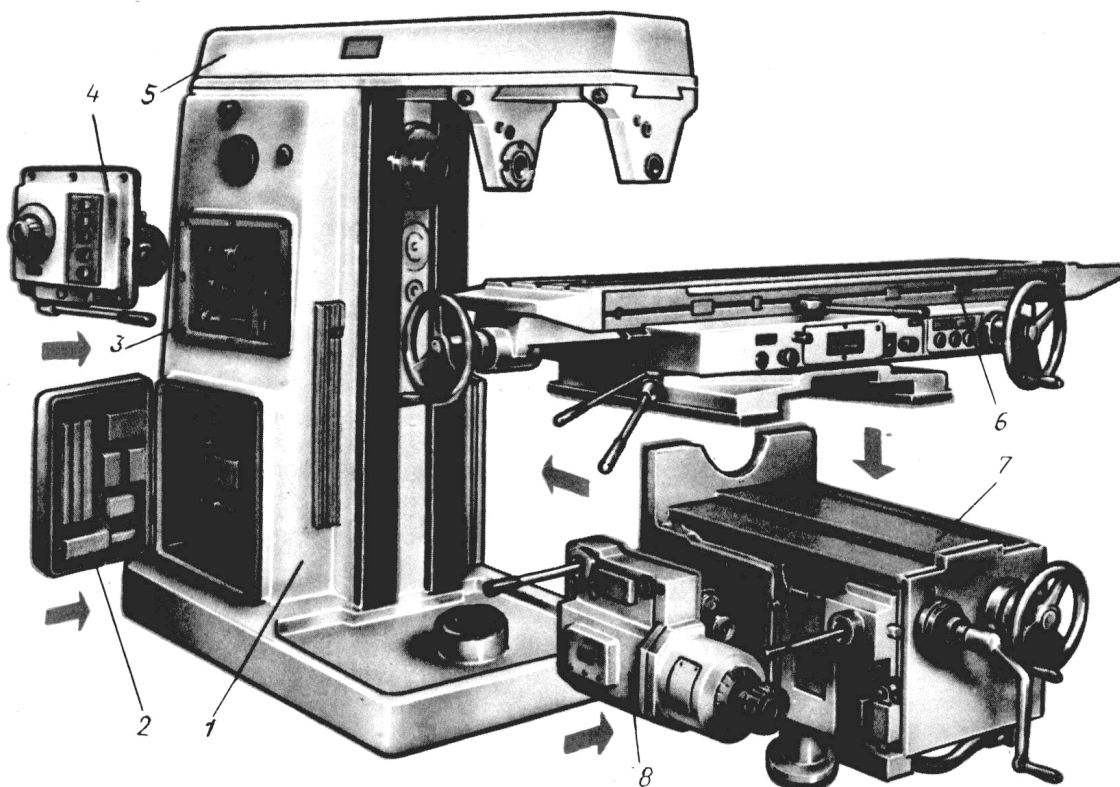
Горизонтально-фрезерний верстат 6Р-82
